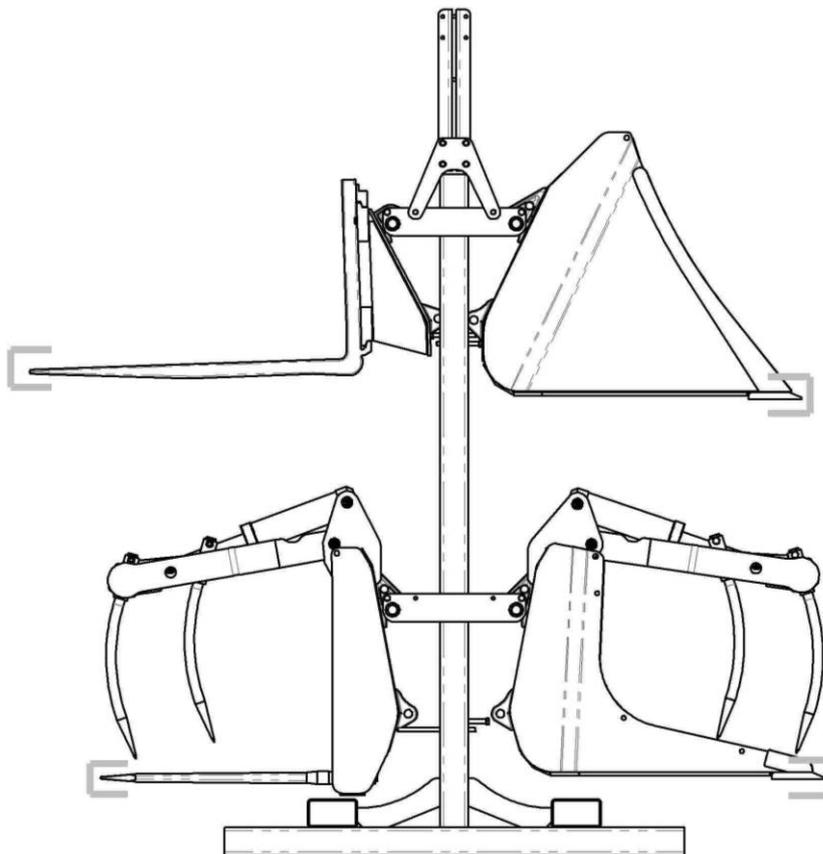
Werkzeugständer bestückt mit vier Frontlader Werkzeugen
